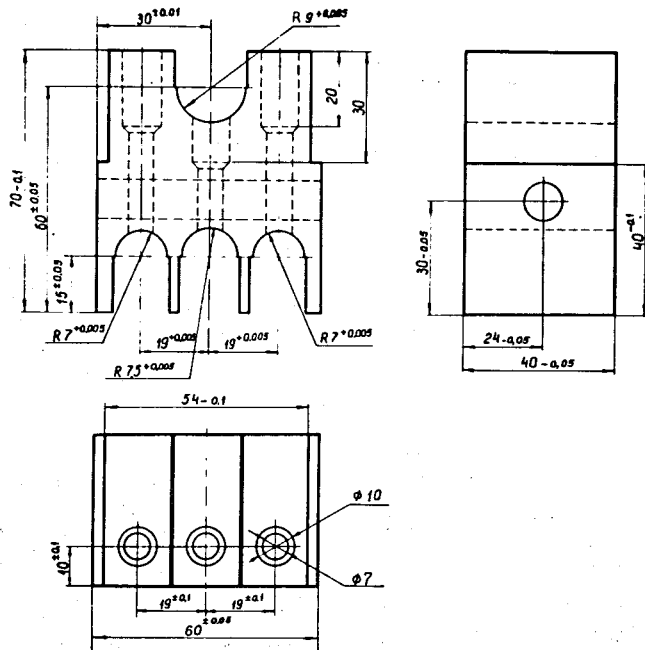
Конструкция фиксатора дрейфовой камеры, изготовленной по новой технологии.
